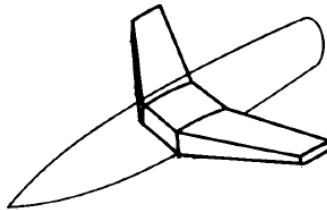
Estructura central del ala tipo carrythrough [9]
